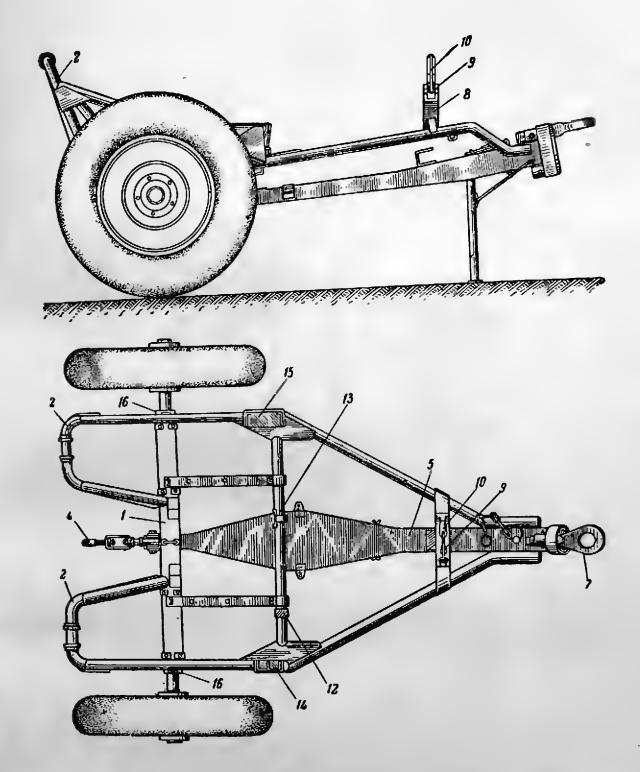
Колесный ход конструкции завода № 702 (общий вид, без ящика для ЗИП):
